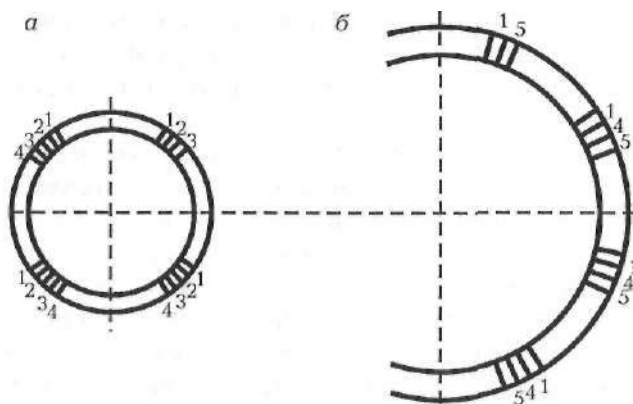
Схема вырезки темплетов для изготовления образцов для механических испытаний при аттестации технологии сварки:
